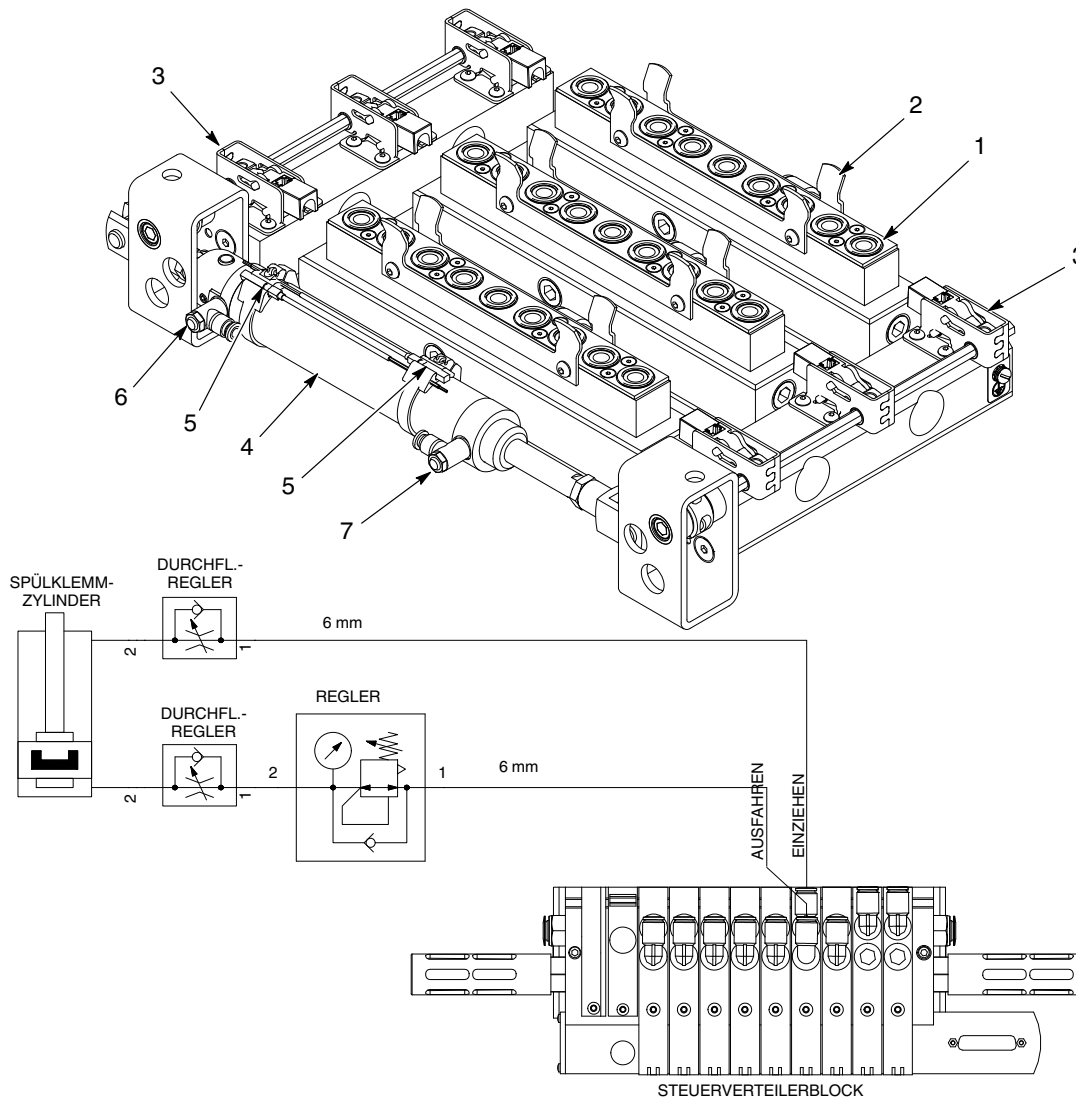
Spülverteilerblock-Baugruppe (3 Klemmbaugruppen abgebildet, Zylinder und Klemmen in Klemmposition)
